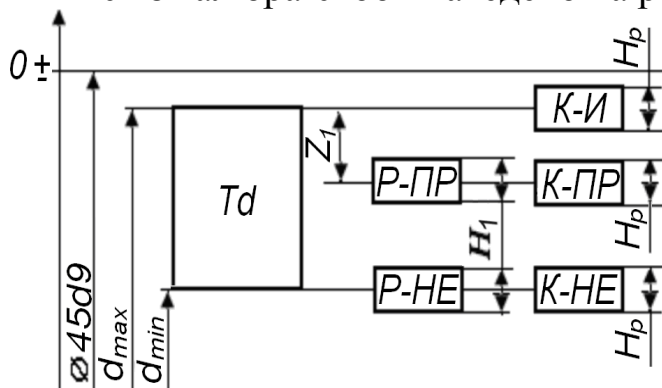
Схема розташування полів допусків контрольованого вала
